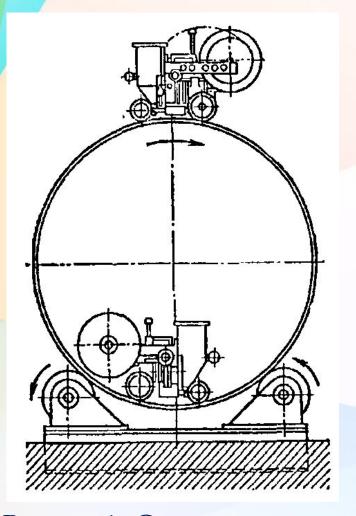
Стенд для сварки кольцевых швов
